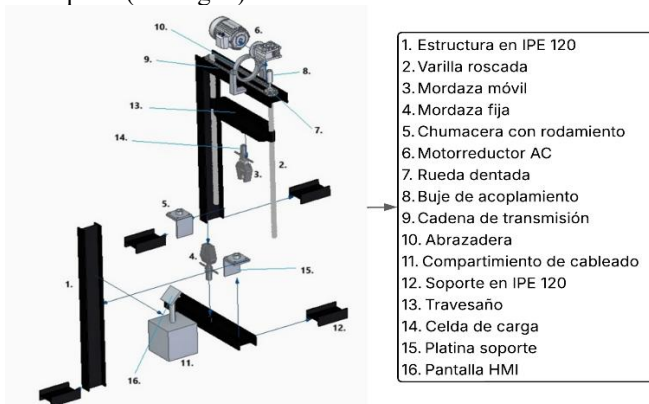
Vista explosionada del diseño. Fuente: Elaboración propia.
